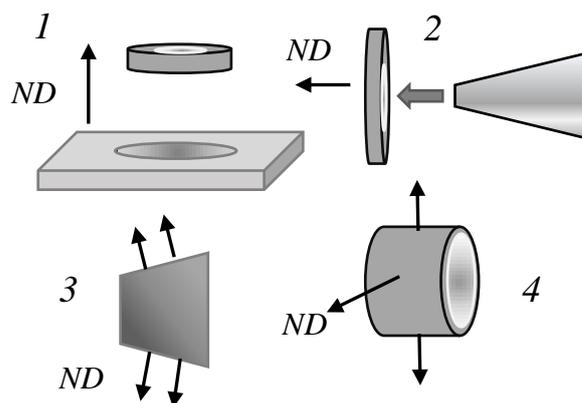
Схема изготовления детали типа «втулка» из плоского кольца
